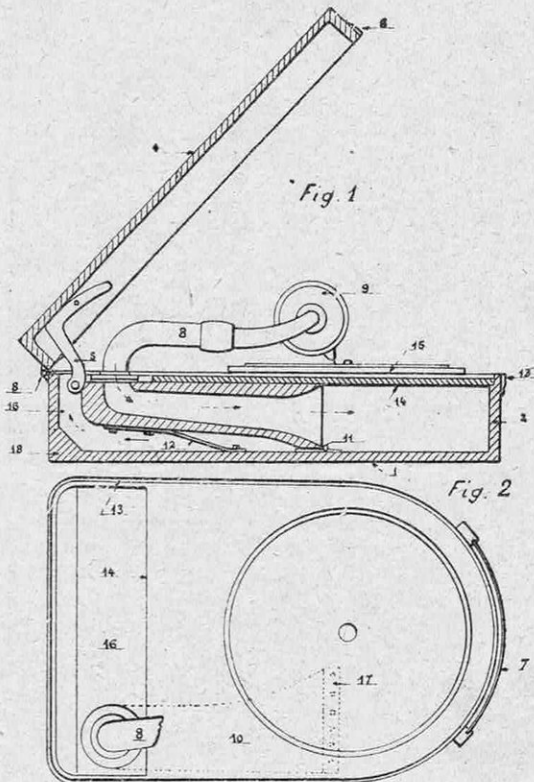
ET 2. — COUPE ET PLAN DU « PARISONOR »
